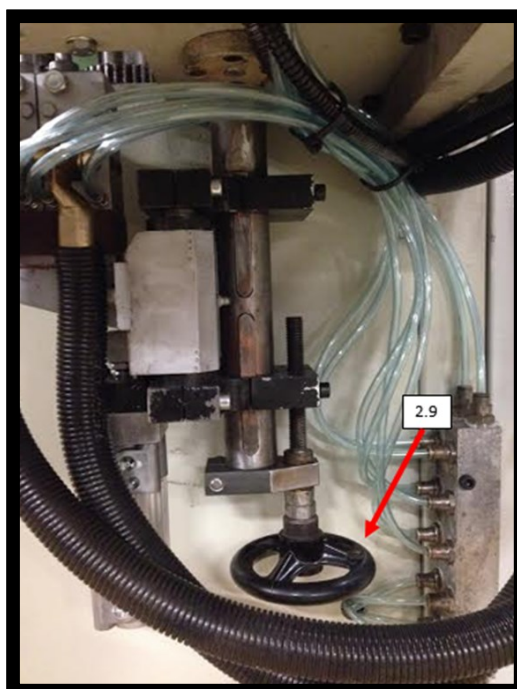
Pontos de ajuste na máquina de marcar a superfície das rolhas (3)
